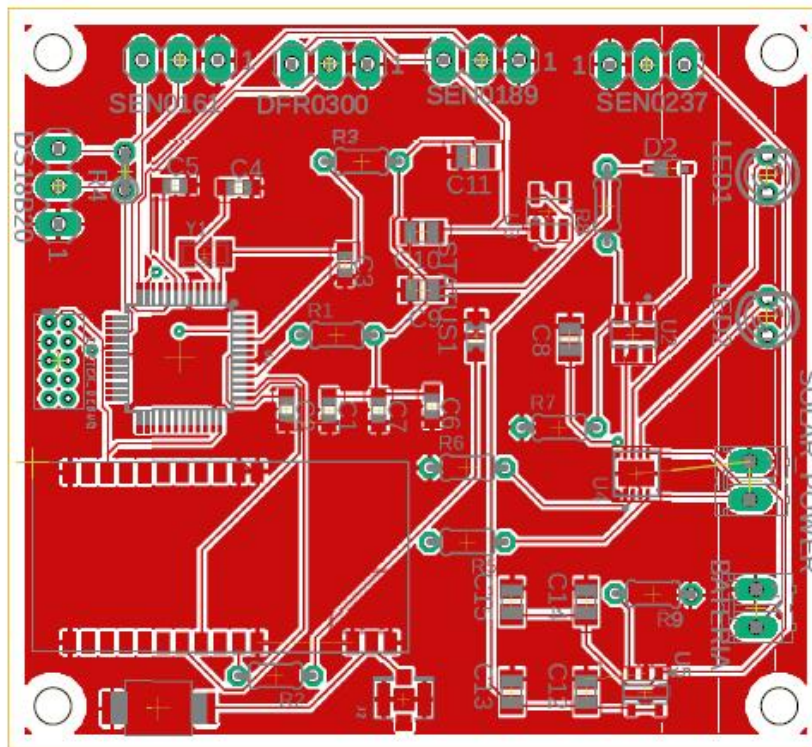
Diseño de la cara top de la PCB de calidad del agua salada
